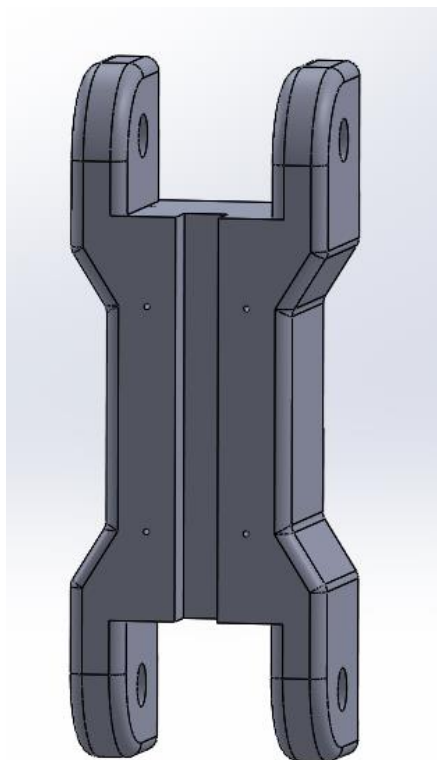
3Д модель корпусу середньої фаланги
